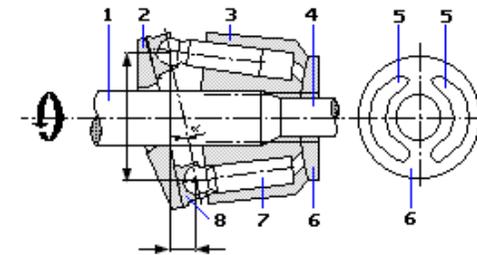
Bomba com disco inclinado 1-eixo de acionamento; 2- disco inclinado; 3- placa; 4- ponta do eixo; 5- rasgos; 6- anel fixo; 7- pistões; 8- placa de união dos pistões.
